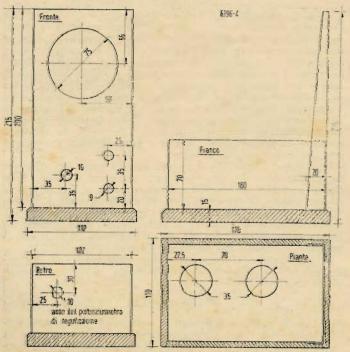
Pianta fronte e profilo del millivoltmetro. Quote in millimetri.
